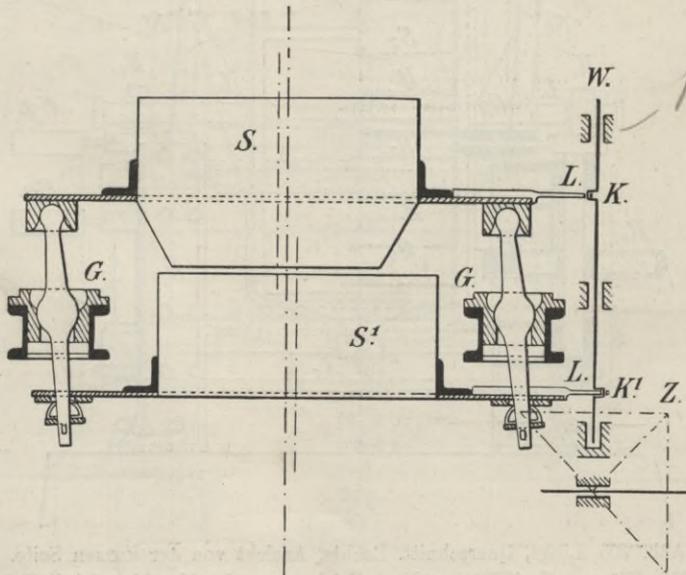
Coxe-Rätter, Prinzip-Skizze.
